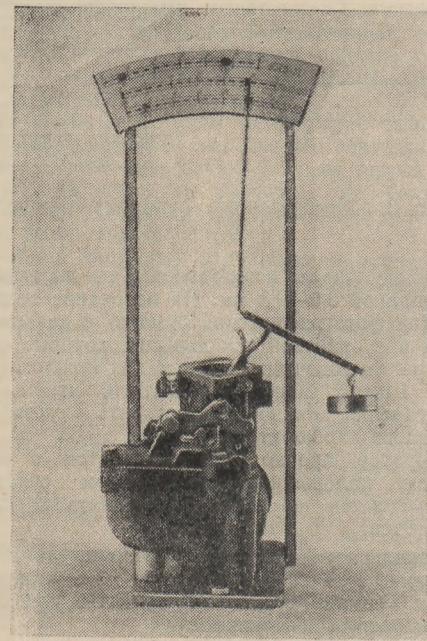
Общий вид установки карбюратора МКЗ-14 на приборе.
